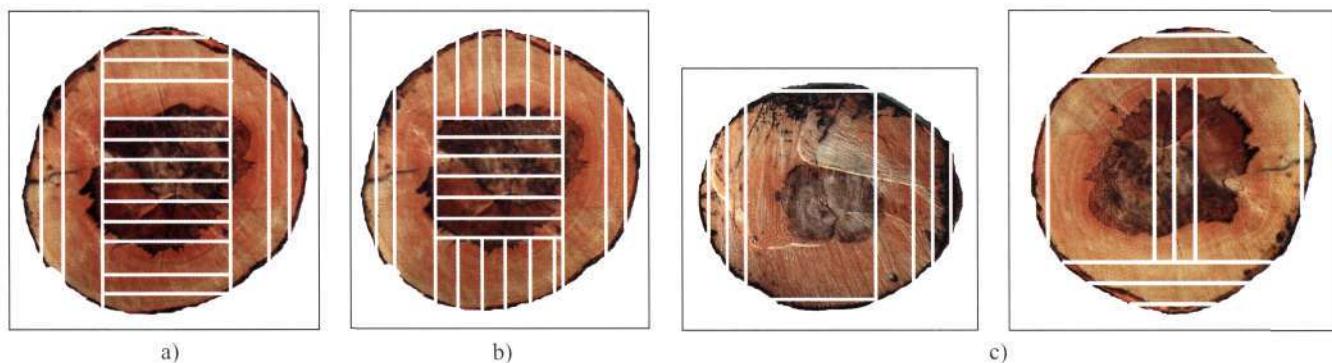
Primjer piljenja bukovih trupaca u cijelo: a) bez nepravе srži, b) sa nepravom srži
